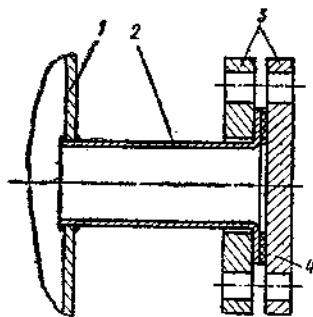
Патрубок подключения вакуум-прерывателя:
